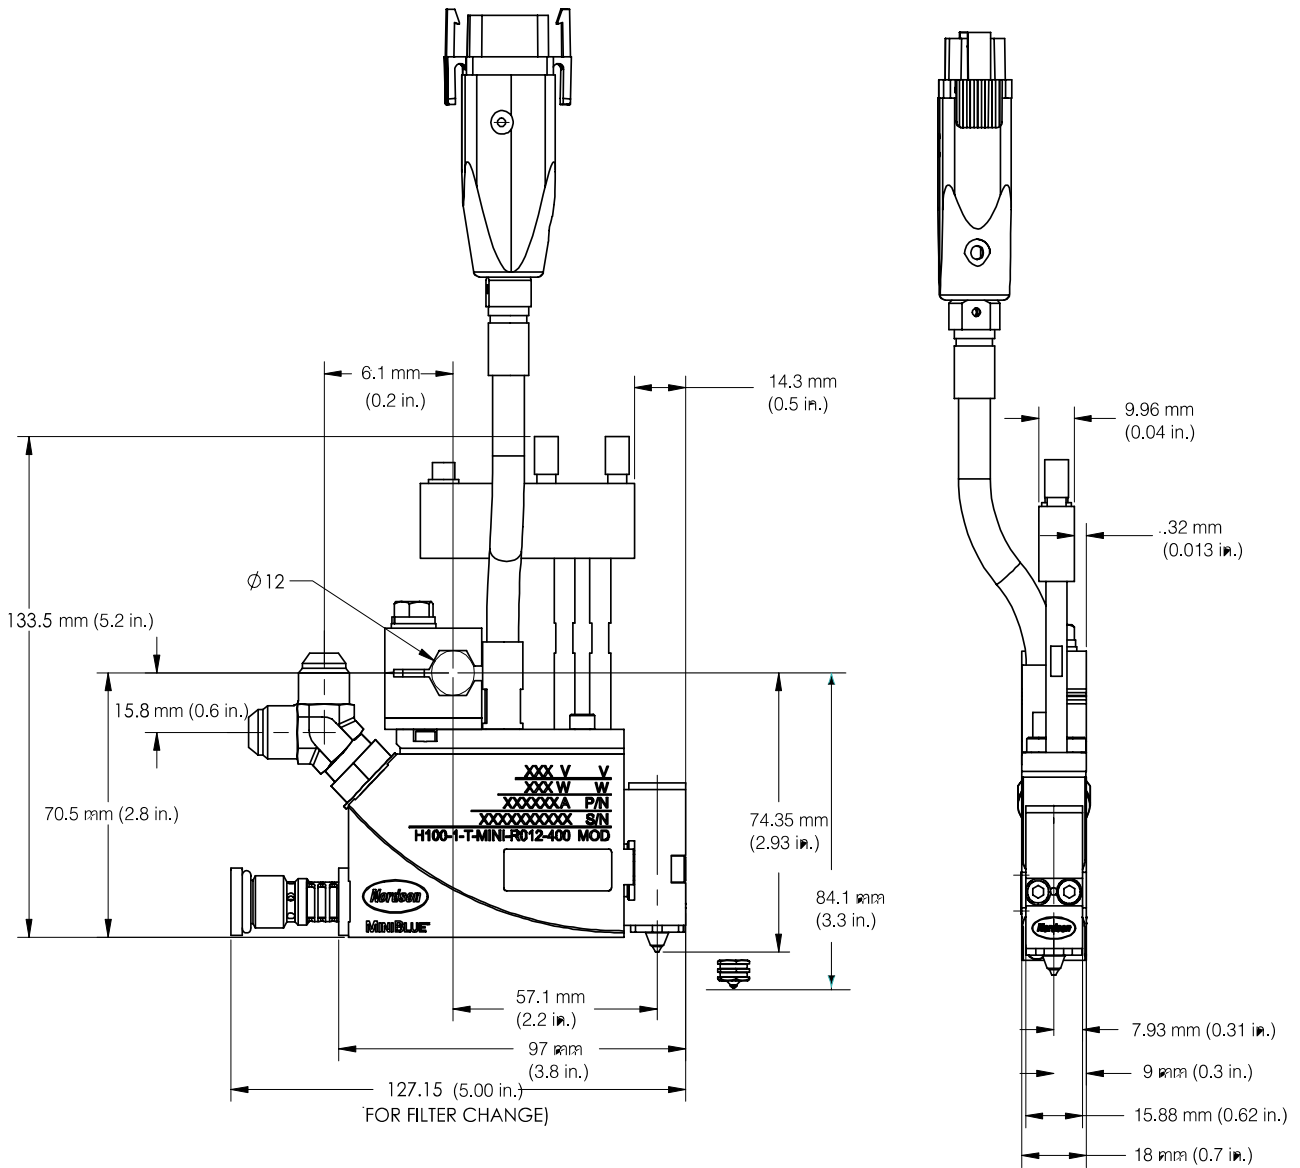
Dimensiones de una pistola delgada de un módulo con una electroválvula SD
